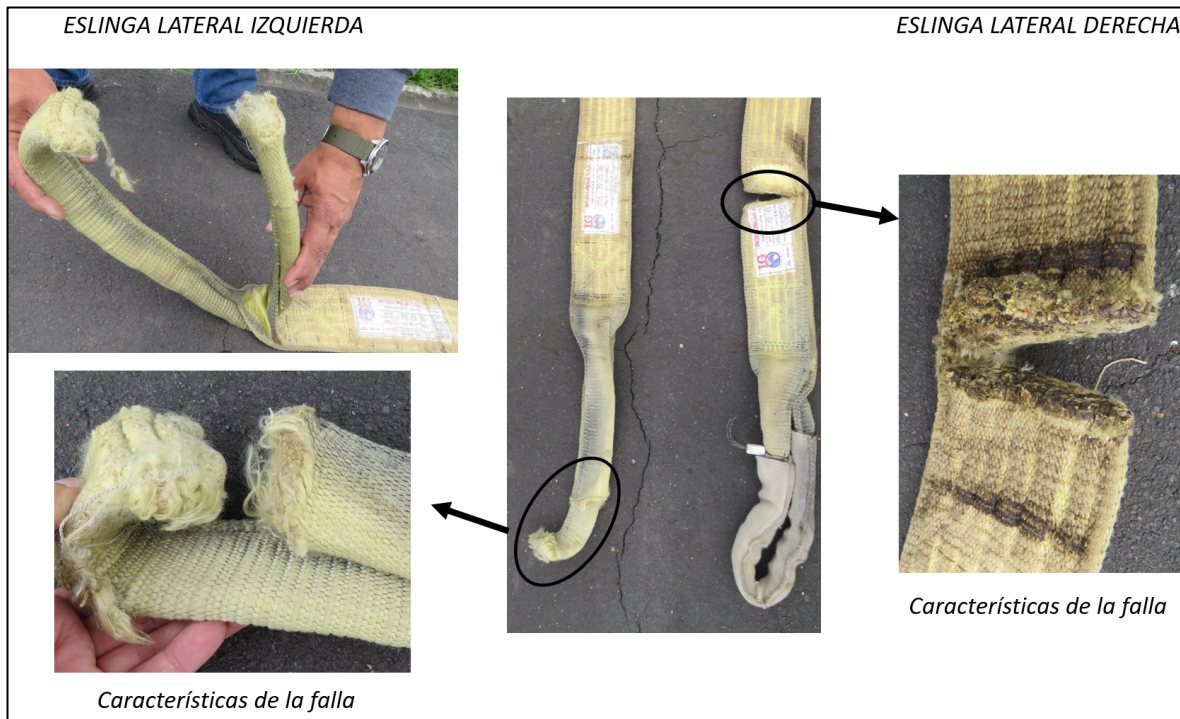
Ubicación y características de falla en las eslingas utilizadas en la operación HK3908
